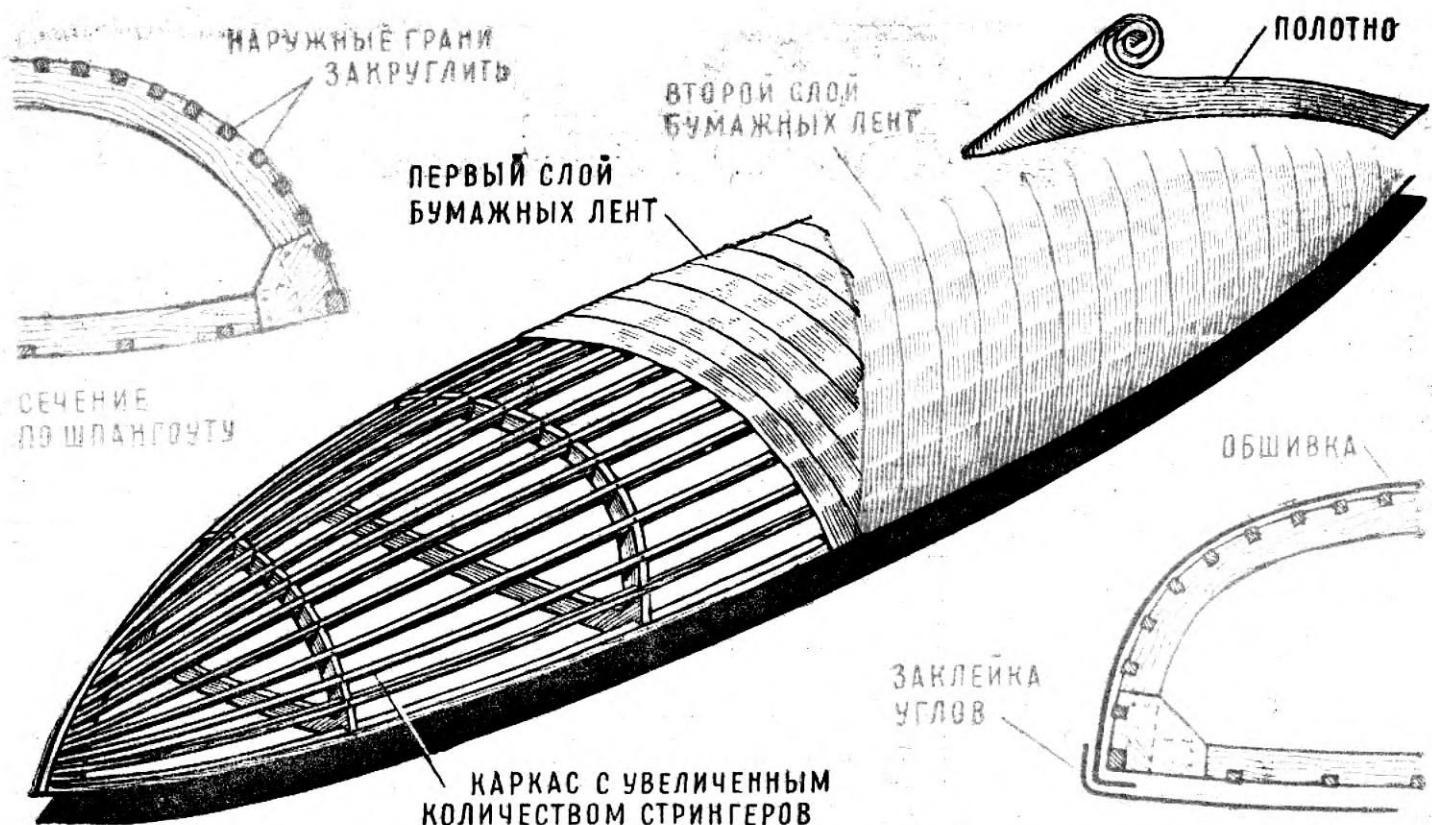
Изготовление обшивки корпуса байдарки (каяка) из крафт-бумажной ленты.
